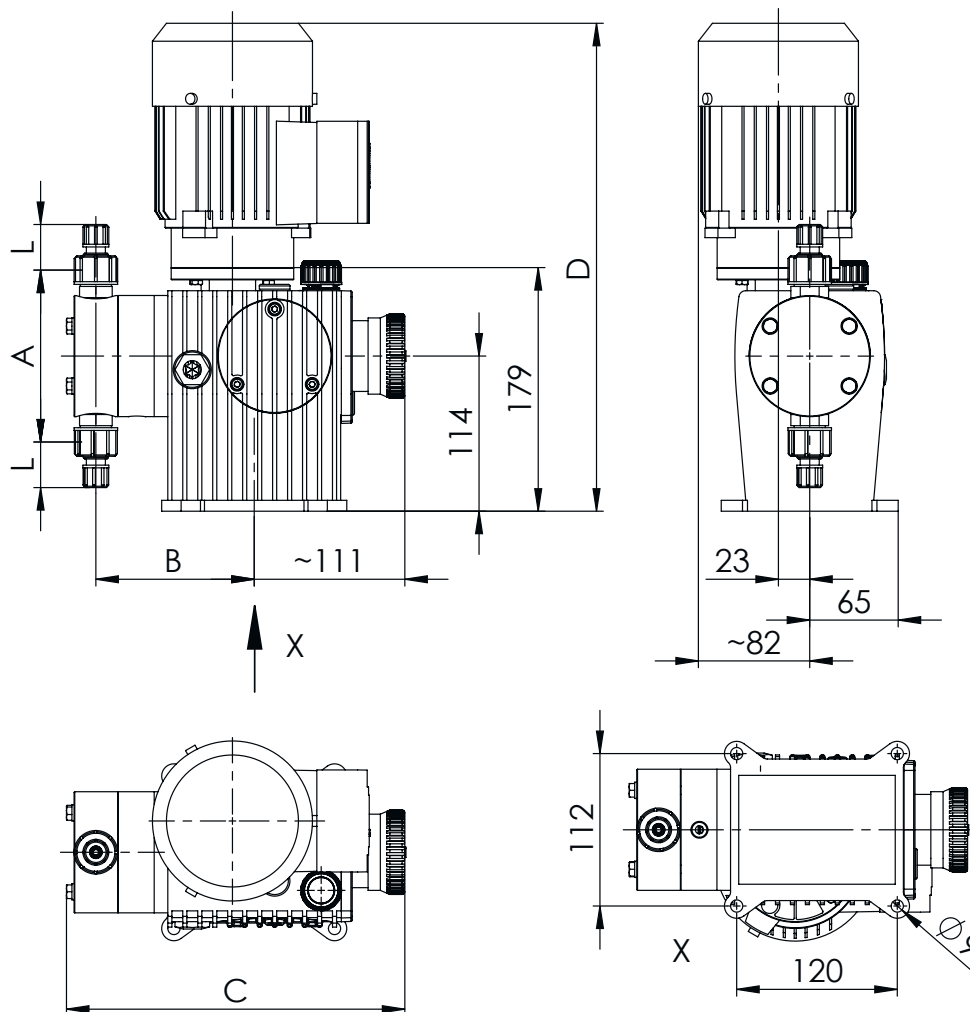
Габаритный чертеж MEMDOS LB 4 – 80, 150
